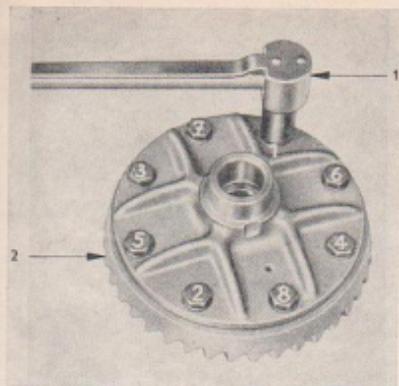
Reihenfolge für das Anziehen der Sechskantschrauben des Tellerrades
